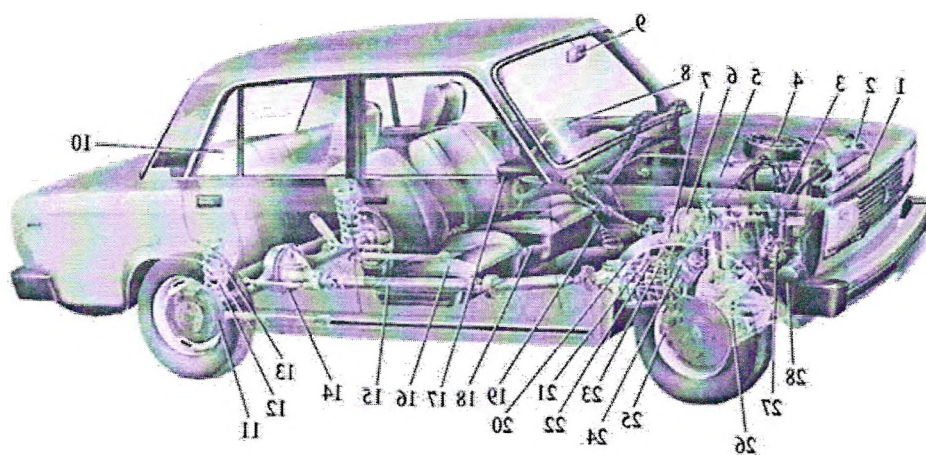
Общий вид легкового автомобиля: 1 — радиатор системы охлаждения; 2 — аккумуляторная батарея; 3 — распределитель зажигания; 4 — воздушный фильтр; 5 — двигатель; 6 — вакуумный усилитель с главным цилиндром гидропривода тормозов; 7 — главный цилиндр гидропривода сцепления; 8 — рулевое колесо; 9 — внутреннее зеркало заднего вида; 10 — заднее сиденье; 11 — задний тормоз; 12 — пружина задней подвески; 13 — амортизатор задней подвески; 14 — задний мост; 15 — карданная передача; 16 — переднее сиденье; 17 — наружное зеркало заднего вида; 18 — рычаг стояночного тормоза; 19 — рычаг переключения передач; 20 — коробка передач; 21 — педаль сцепления; 22 — педаль тормоза; 23 — педаль акселератора («газа»); 24 — картер рулевого механизма; 25 — передний тормоз; 26 — пружина передней подвески с амортизатором; 27 — топливный насос; 28 — масляный фильтр
